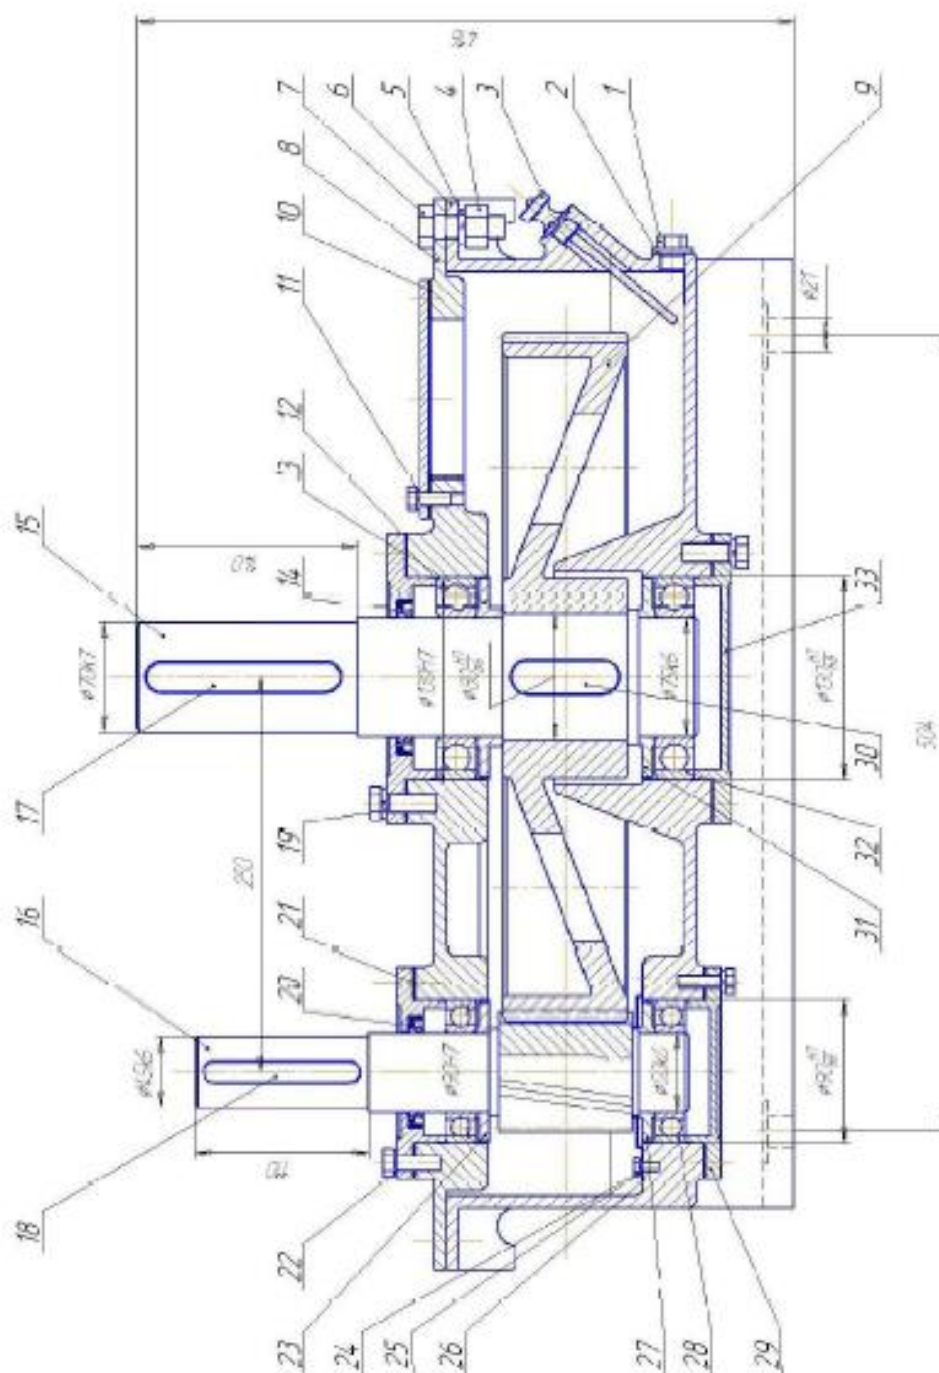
Редуктор цилиндрический одноступенчатый горизонтальный с вертикальным валом (вид сверху)
